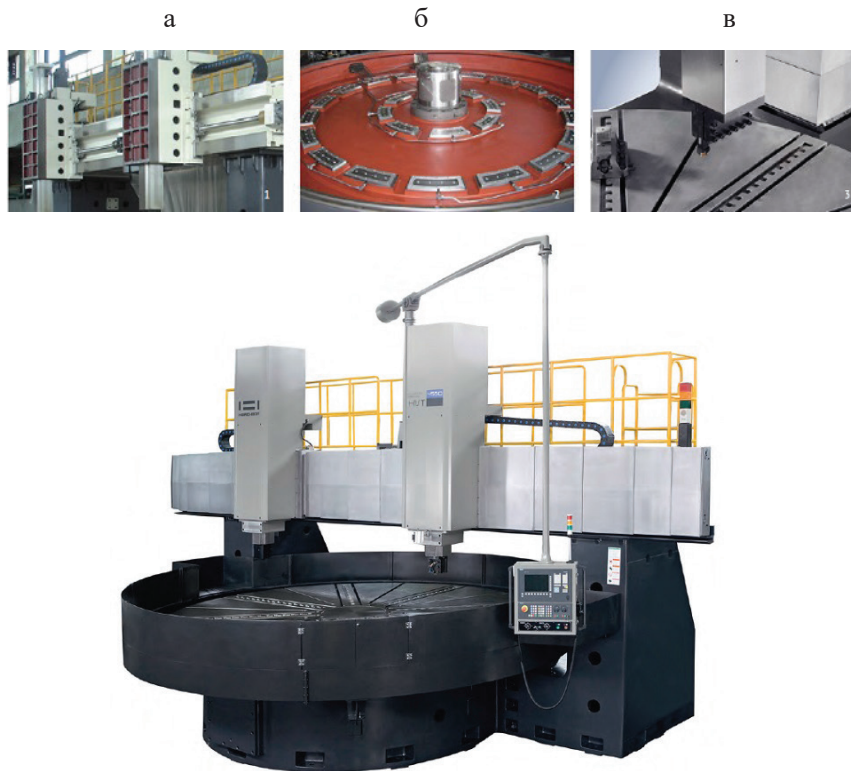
Токарно-карусельний верстат з ЧПУ з нерухомою траверсою Hwacheon HVT-6080
